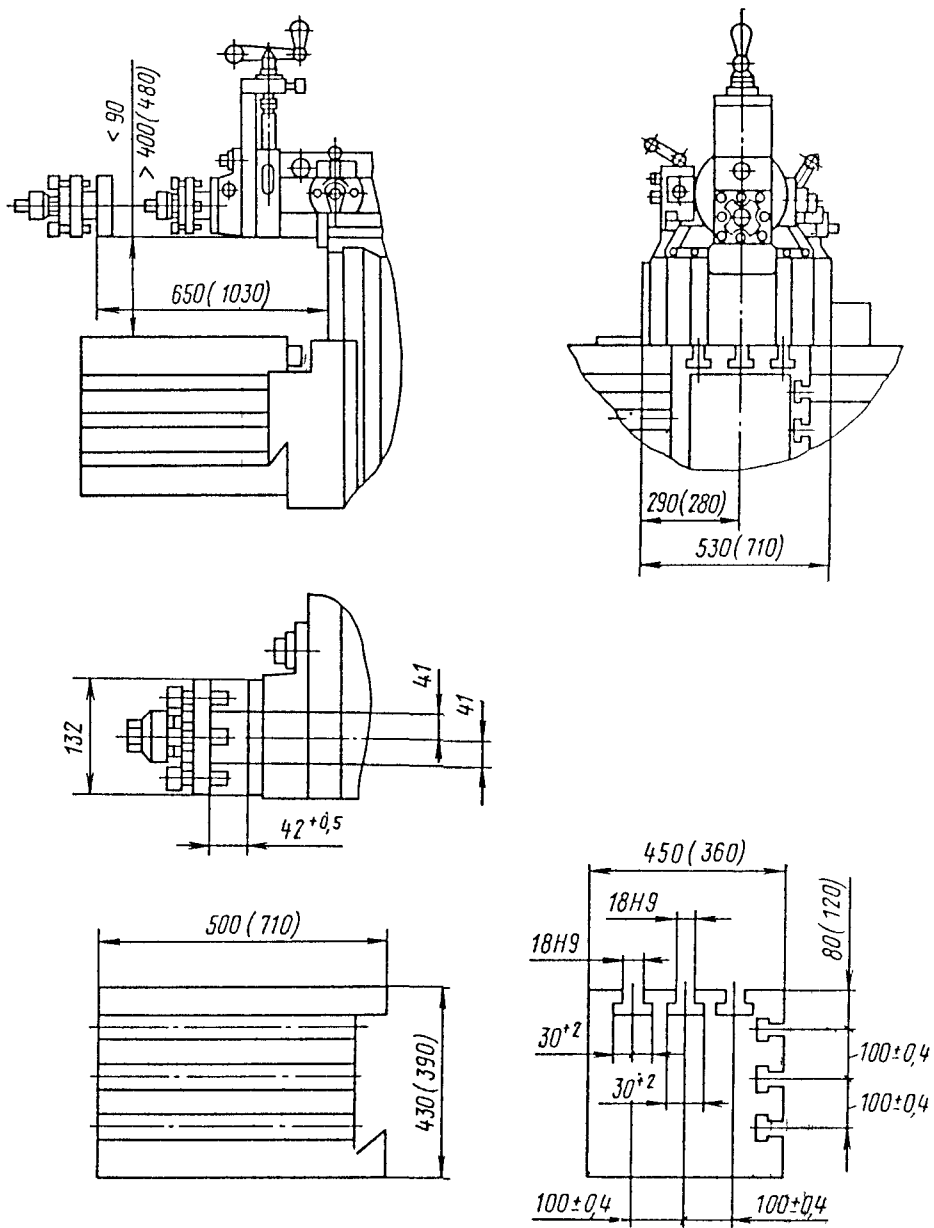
Габаритные размеры рабочего пространства и присоединительные размеры
